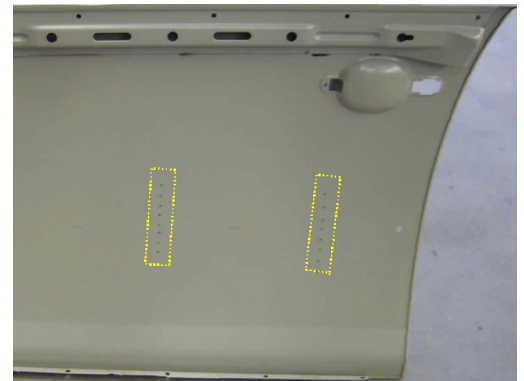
Rückseite eines Tür außenbleches mit Hinterbrand (gelbe Markierung)
